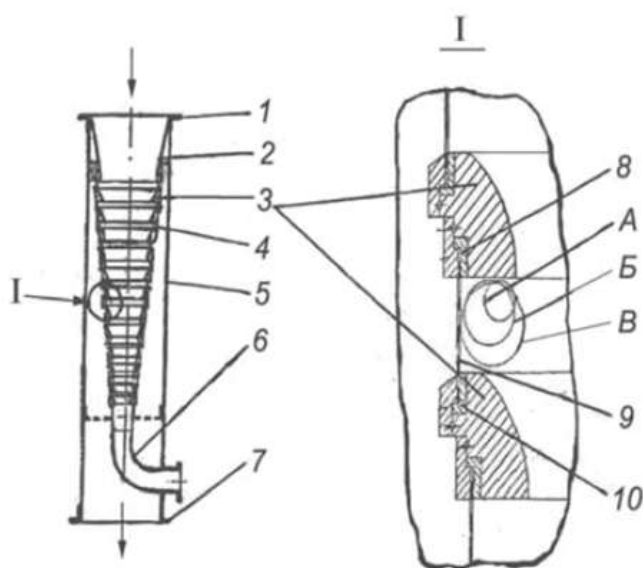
Вихрединамический воздушный фильтр-пылеулавливатель
